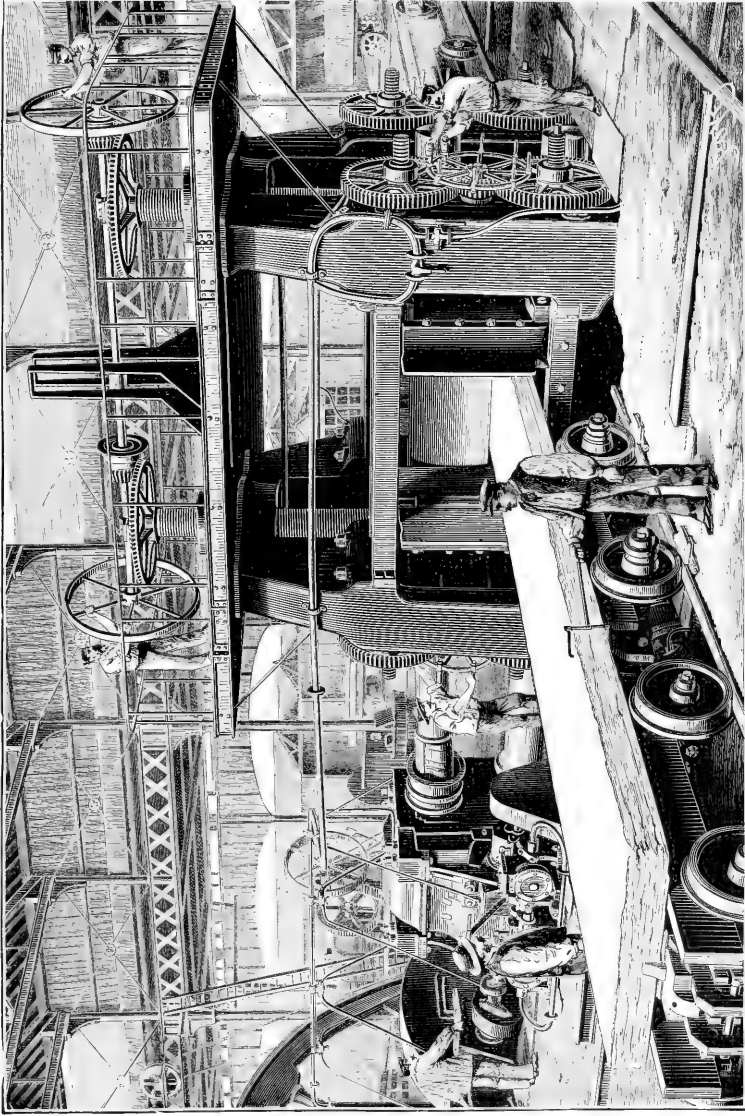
Vue du grand Laminoir pour la fabrication des plaques de blindage, de l'usine des Etaings (Marret frères). — Le laminage d'une plaque en fer vient d'être terminé et l'ouvrier présente sa jauge pour vérifier si l'épaisseur voulue est atteinte. — La longueur maximum entre les cylindres verticaux est de 3^m200 et la hauteur maximum entre les cylindres horizontaux est de 1^m300. Le poids d'une cage nue est de 43.000 kilogrammes et celui de chaque cylindre horizontal de 30.000 kilogrammes.
